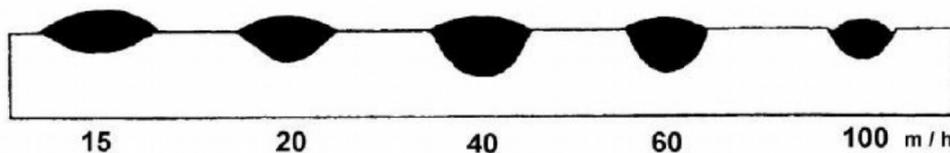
Efecto de la velocidad de soldadura sobre el aspecto del cordón.
